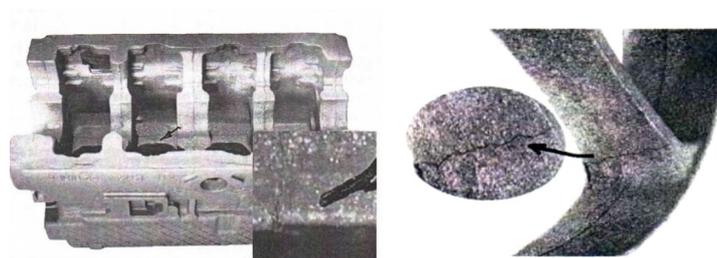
Дефект отливки «Холодная трещина»
